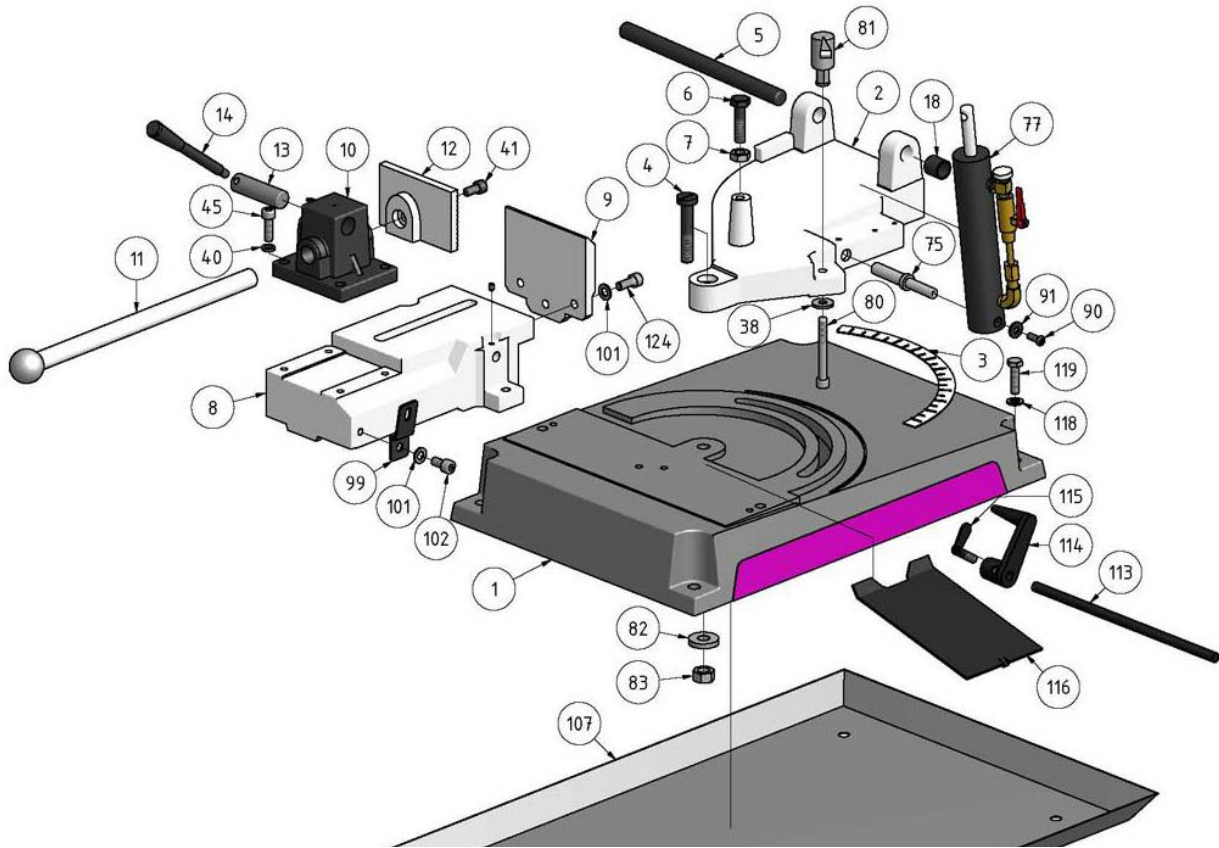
Ersatzteilzeichnung 3 von 4 - Parts drawing 3 of 4
